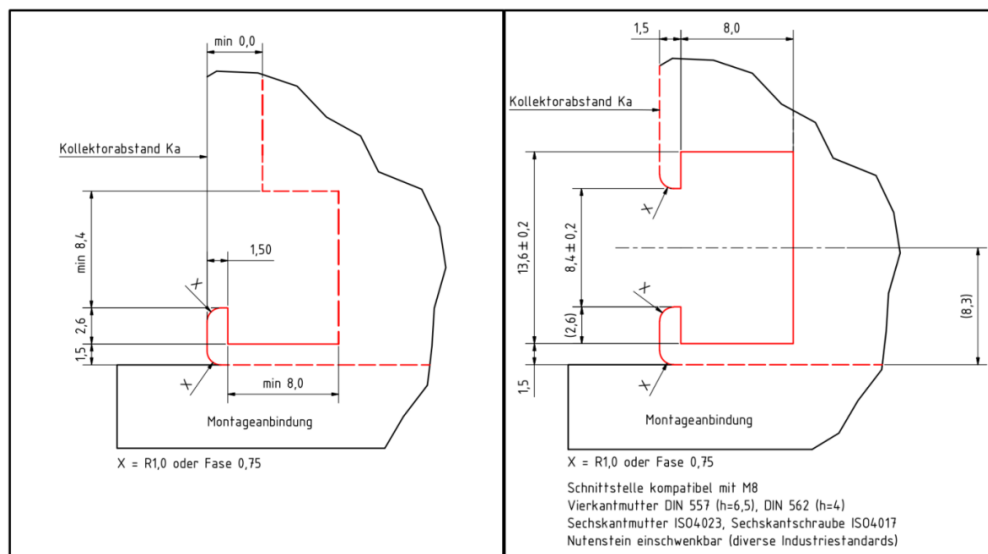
Festgelegte Standard Schnittstellen für die Kollektorbefestigung in Form von fertigungsgerechten Zeichnungen als MOUNT-L (links) oder optional MOUNT-C (rechts)
